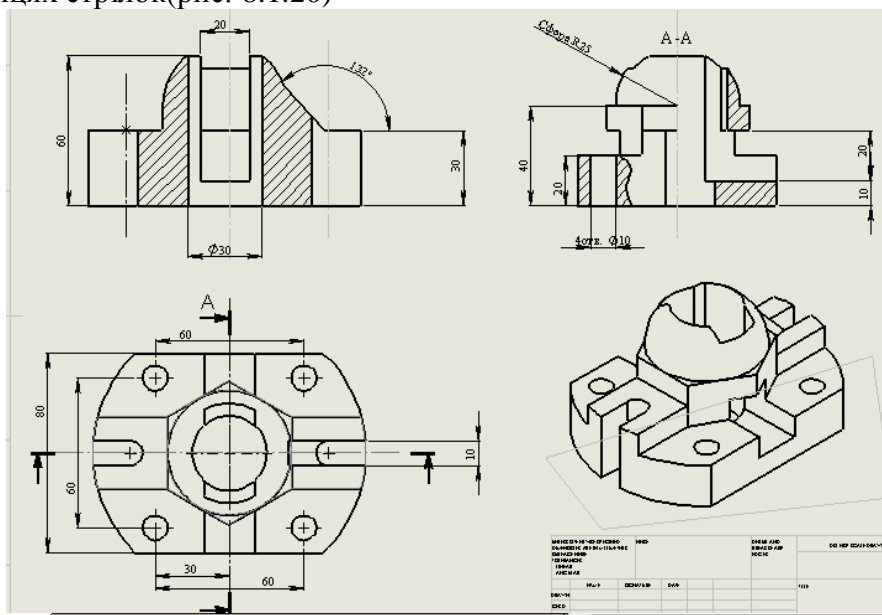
Простановка розмірів інструментом АВТОРАЗМЕР (Smart Dimension)
